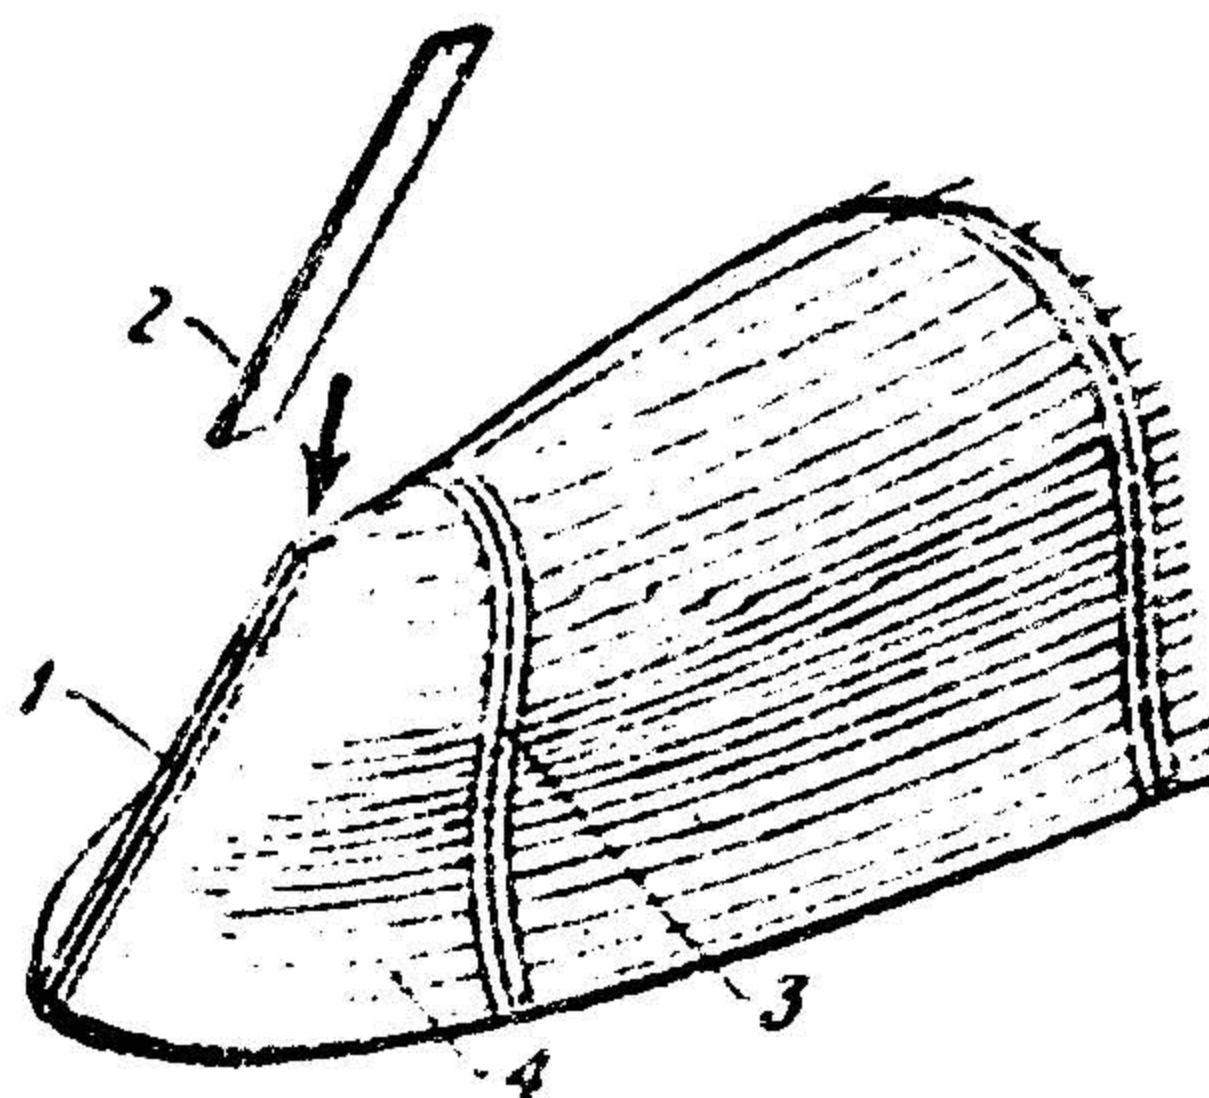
Установка на болванке носовой полосы: 1 — паз; 2 — полоса; 3 — шпангоут; 4 — болванка
